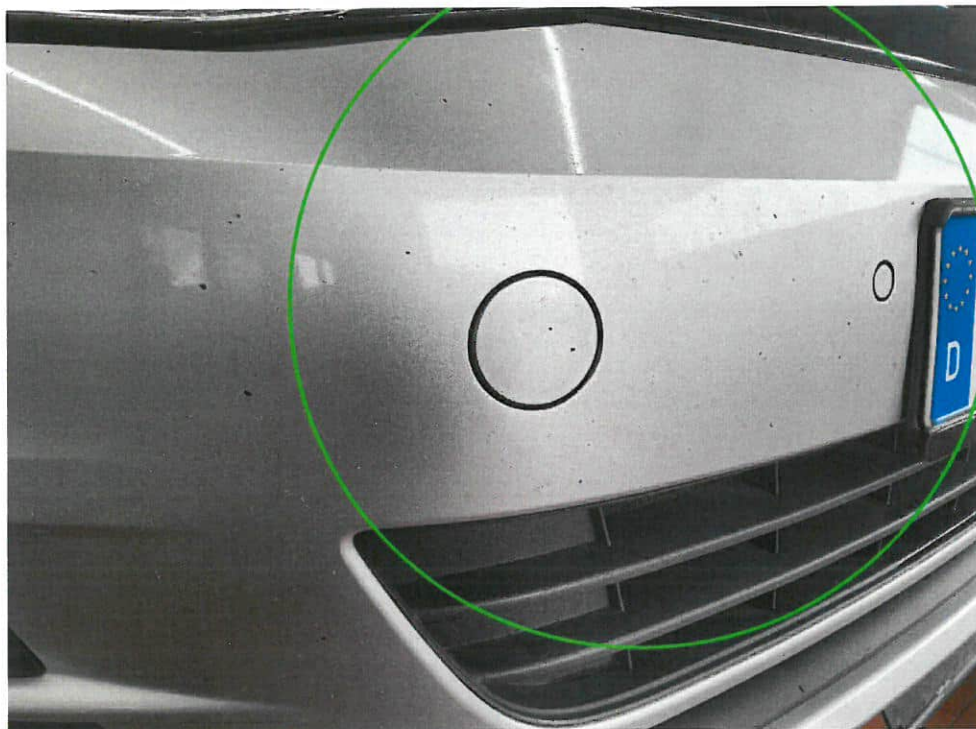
Stoßfänger vorne Lackierung, viele Steinschläge, lackieren
